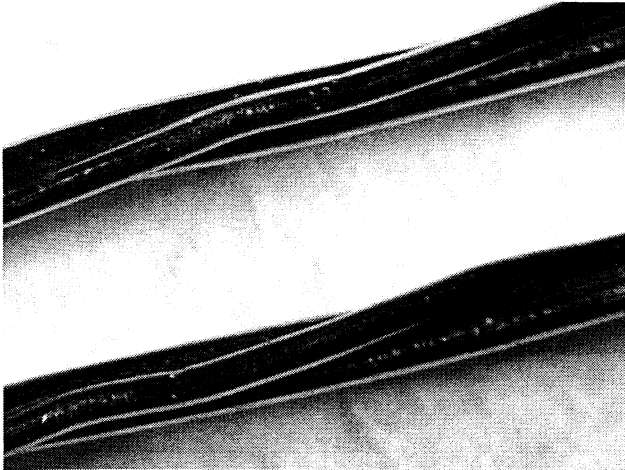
Внешний вид металлокорда 3x0,30 HT FRP
